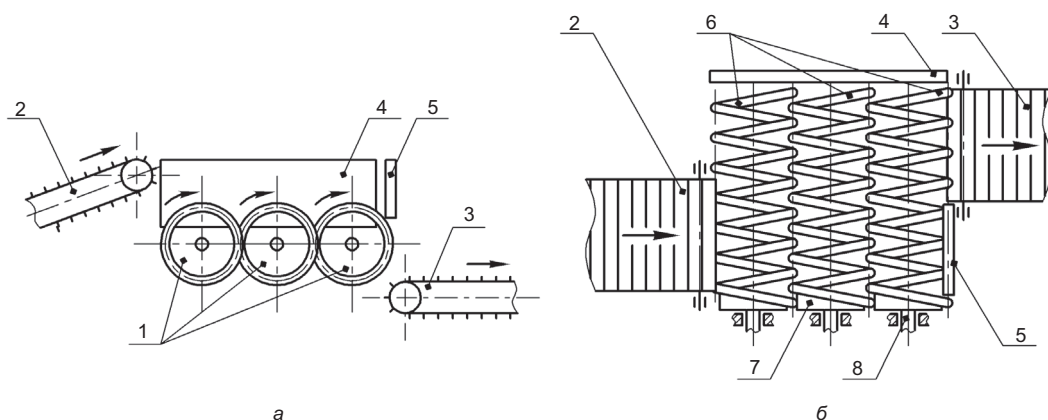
Конструктивна схема очисника картоплі спірального типу: а — вид збоку; б — вид зверху; 1 — валець, що складається із приводних очисних спіралей; 2 — завантажувальний елеватор; 3 — вивантажувальний елеватор; 4, 5 — захисні екрани; 6 — консольні кінці очисних спіралей; 7 — закріплені кінці спіралей; 8 — вали, які приводять спіралі в обертальний рух
